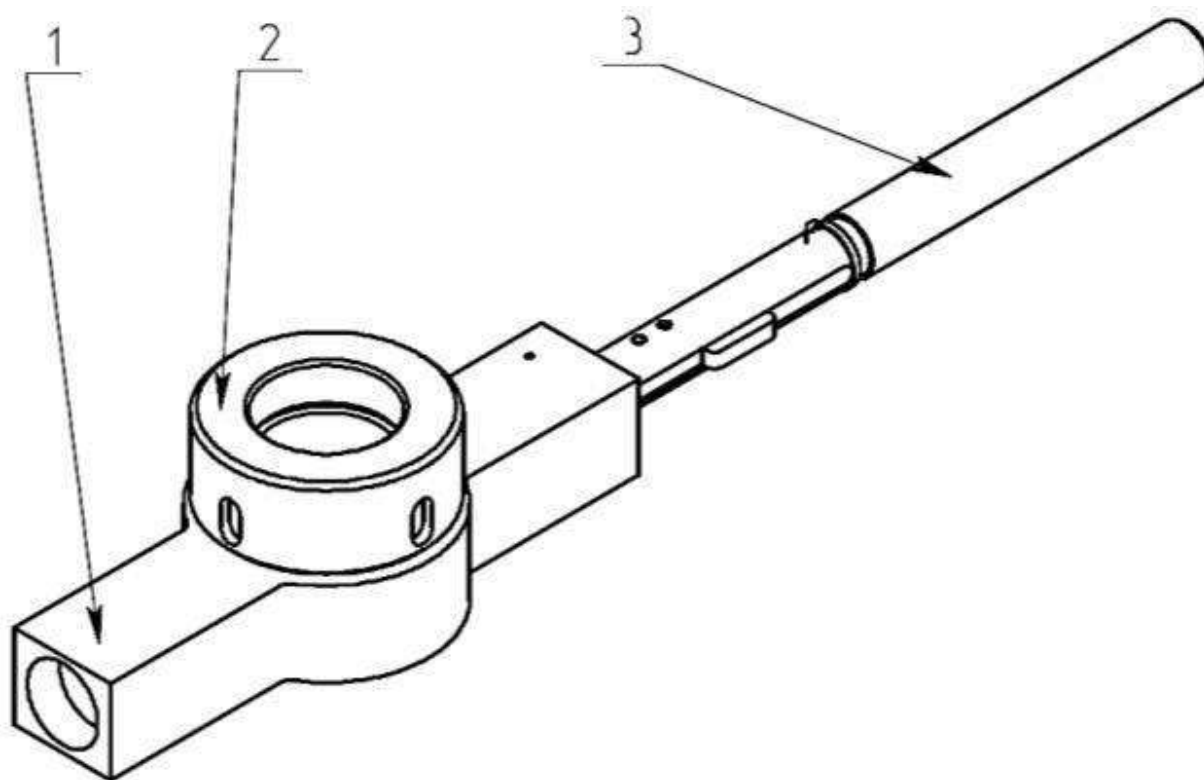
Корпус для кріплення трьох нижніх кульок
